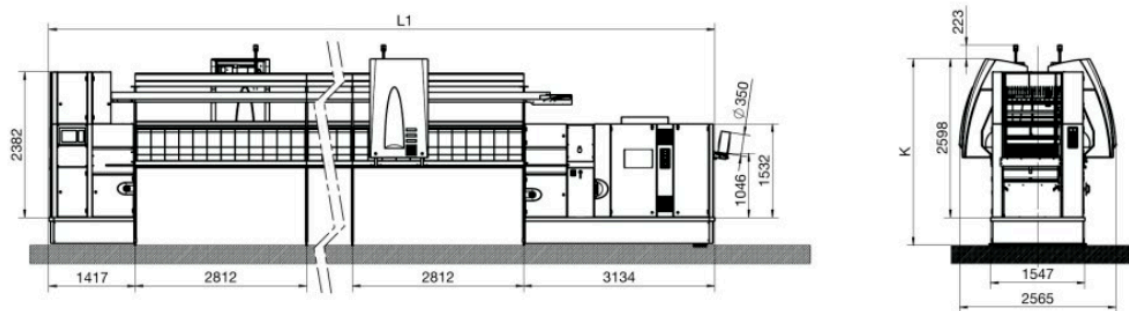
Desenho industrial da Máquina de fiar a rotor automática, Autocoro ACO 9 480, marca SAURER.
